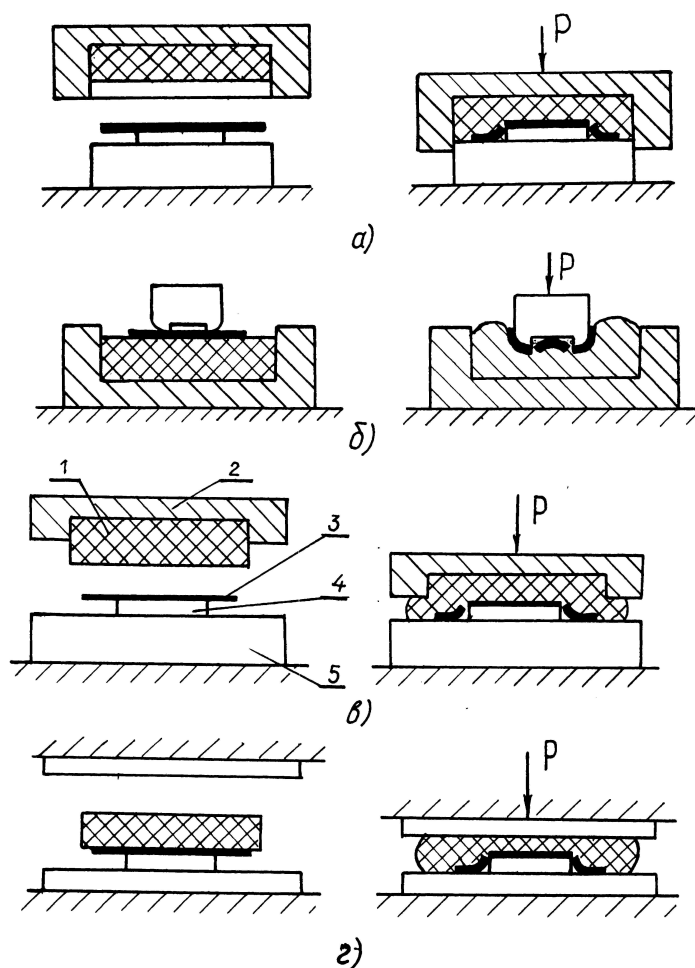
Схемы способов штамповки деталей эластичной средой:
